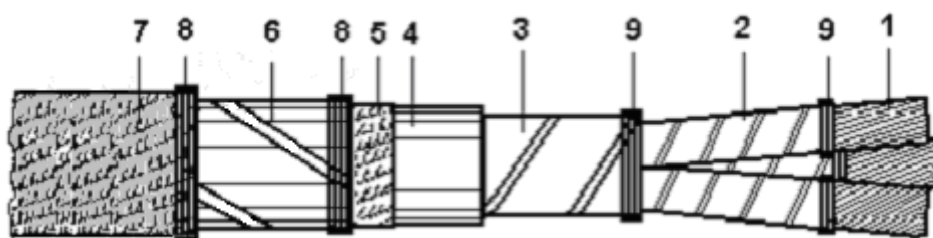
Общий вид разделанного трехжильного кабеля с бумажной изоляцией: 1- токопроводящие жилы; 2 – фазная изоляция; 3 – общая (поясная) изоляция; 4 – герметичная оболочка; 5 – подушка под броней; 6 – броня из стальных лент; 7- наружный защитный покров; 8 – проволочный бандаж; 9 – бандаж из ниток
